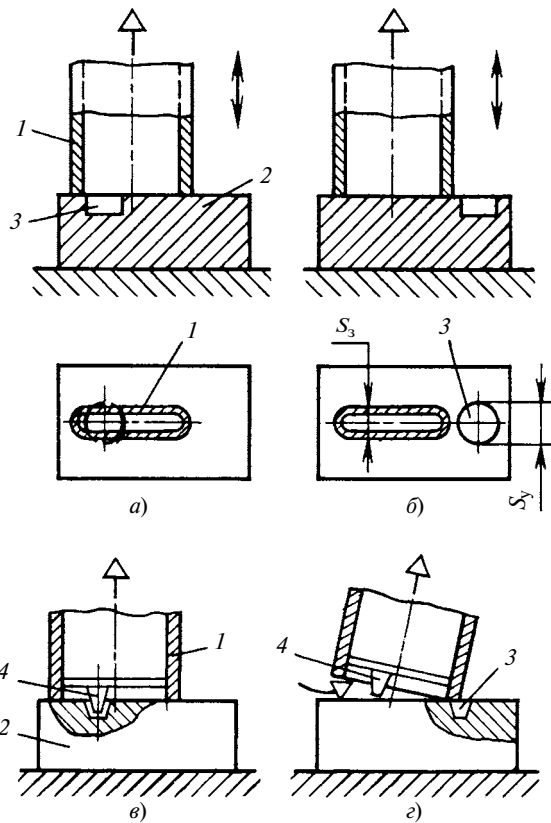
Схемы сортировки деталей с помощью вакуумного захвата: *a, б* — щелевидного; *в, г* — с иговым шупом; *1* — вакуумный захват; *2* — деталь; *3* — углубление; *4* — иговым шуп
